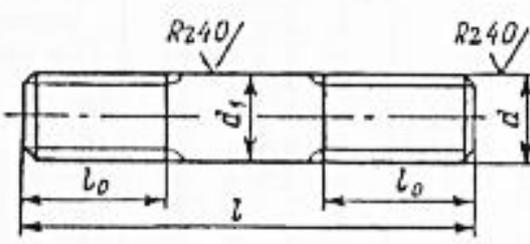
Шпильки нормальной точности для деталей с гладкими отверстиями
